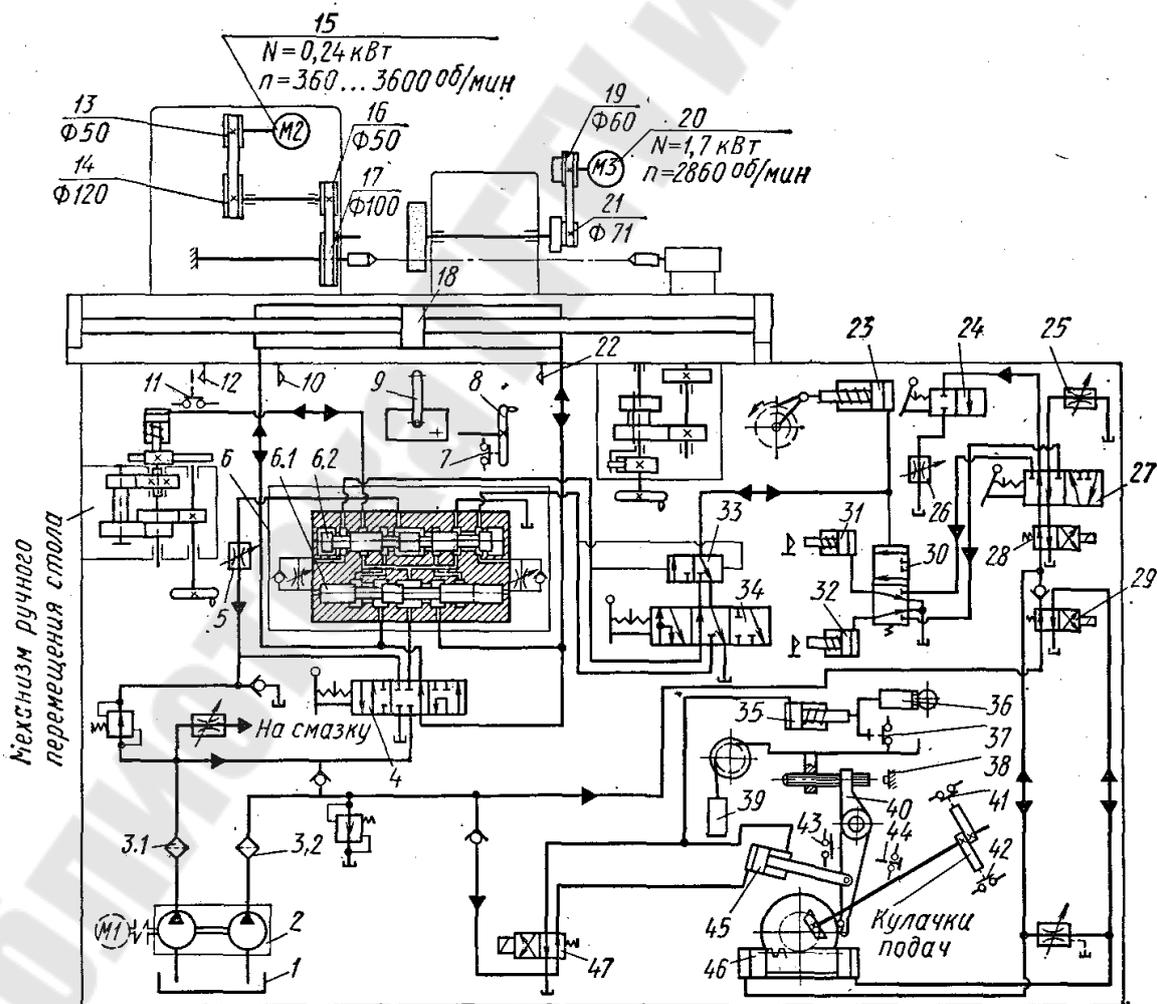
Принципиальная схема круглошлифовального центрового станка
